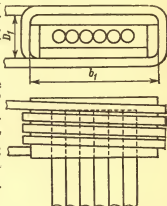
Овальный индуктор для нагрева цилиндрических заготовок
